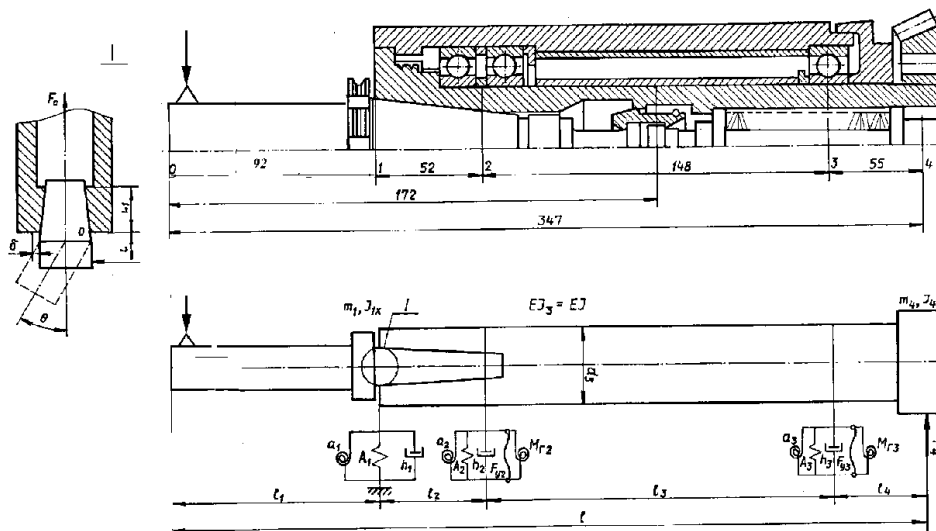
Шпindelний вузол: конструктивна та розрахункова схеми
